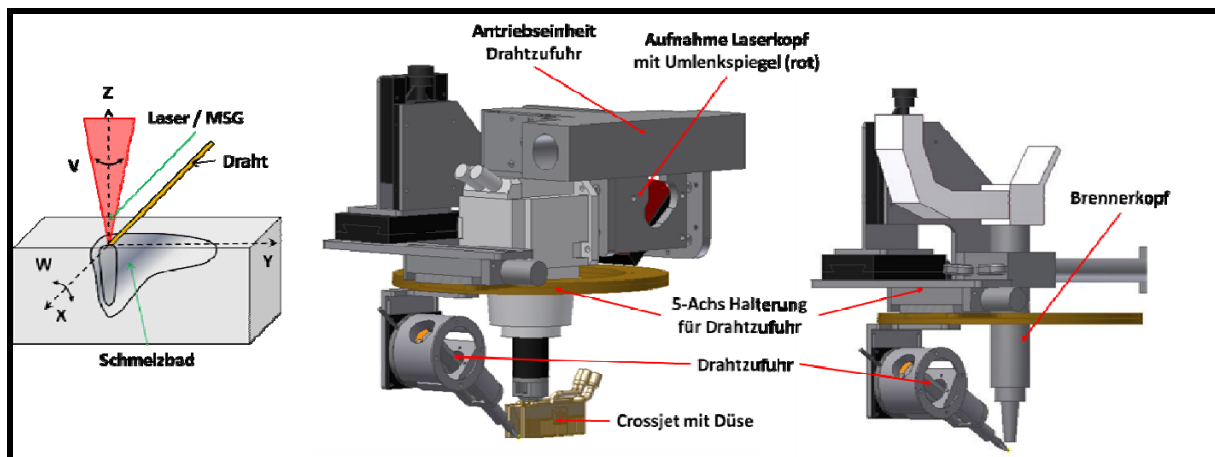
Halterung der Drahtzufuhr: links für das Laserstrahlschweißen, rechts für das MSG-Schweißen
